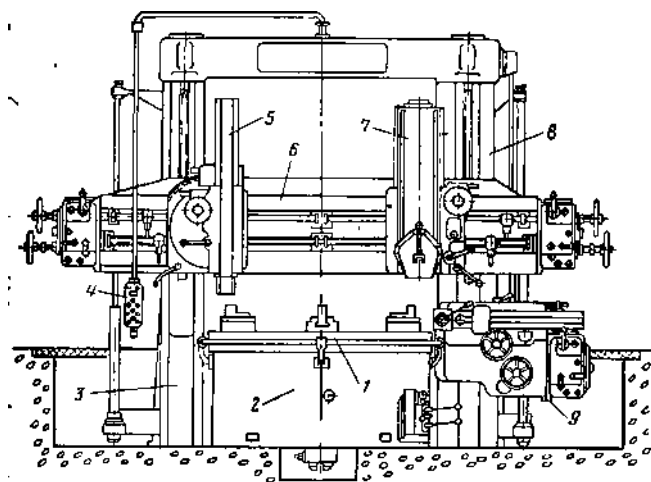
Общий вид тяжелого карусельного станка модели 1553.
